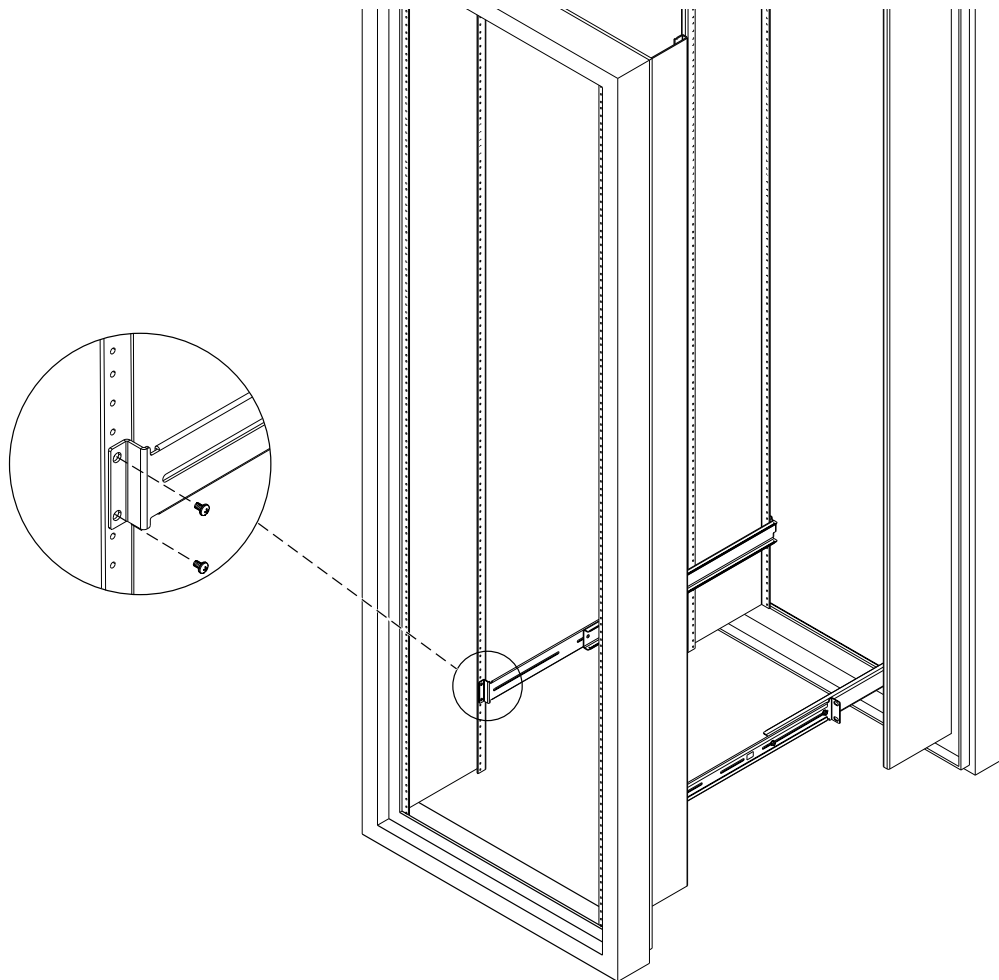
Fixation des supports guidés sur un châssis Sun StorEdge de 72 pouces de hauteur – Vue arrière (panneaux latéraux retirés à des fins de clarté)
